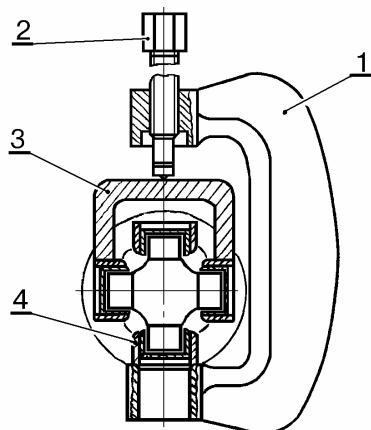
Выпрессовка подшипников крестовины 2105/21211-2202025.
